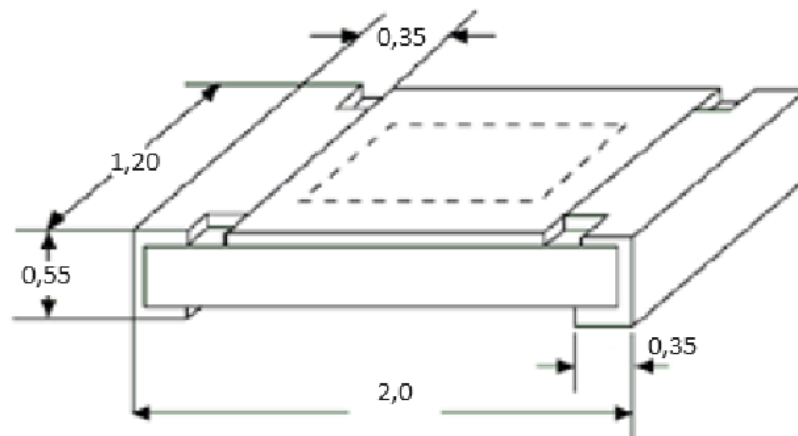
Зовнішній вигляд та габаритні розміри резистора в корпусі RC0805
